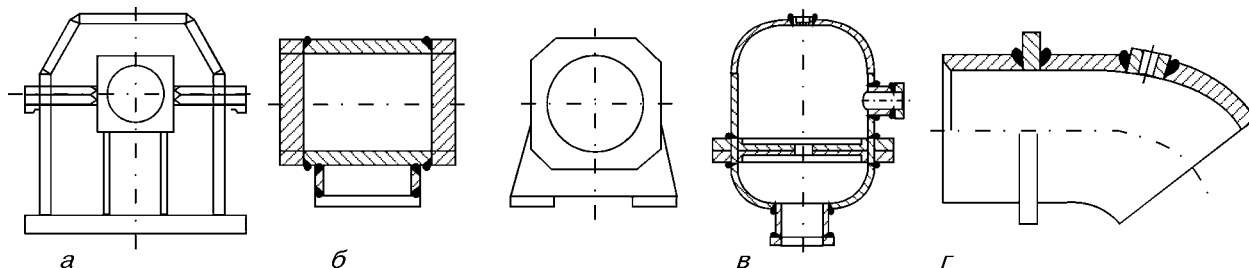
Типы сварных корпусов: а — коробчатый; б — цилиндрической формы; в — с торовыми поверхностями; г — сочетание цилиндра с фланцем
